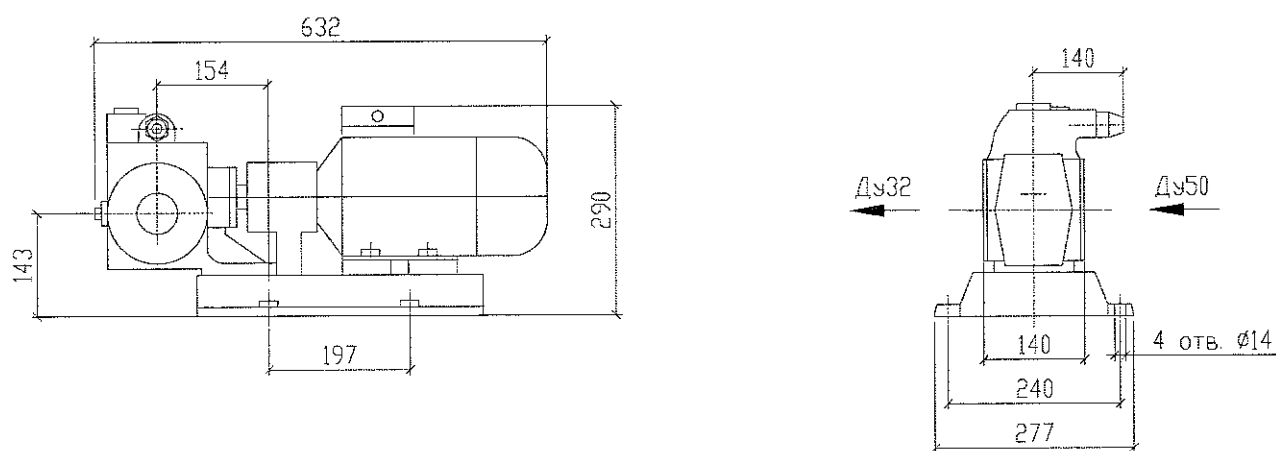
Габаритный чертеж насоса откачки дренажей
